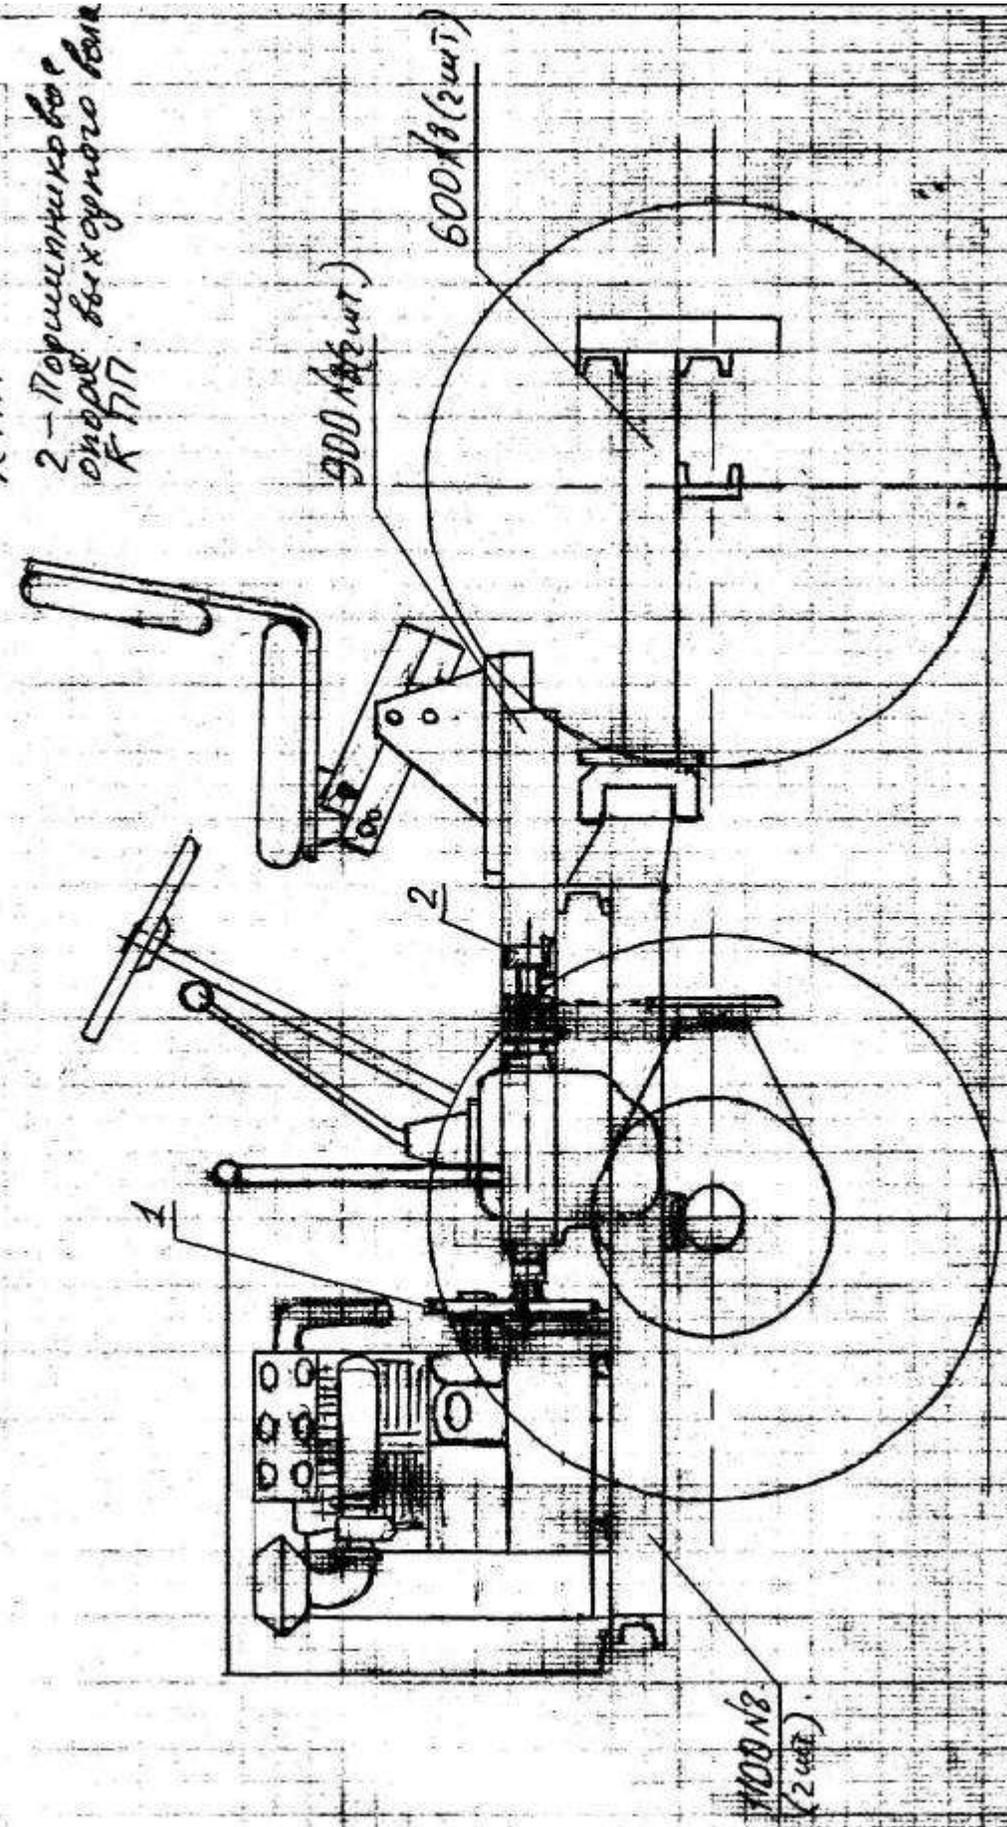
Габаритный чертёж мини-трактора (Вид сверху)
